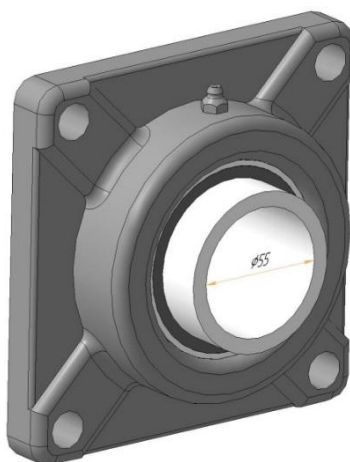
Подшипниковый узел серии UCF под диаметр 55 мм
